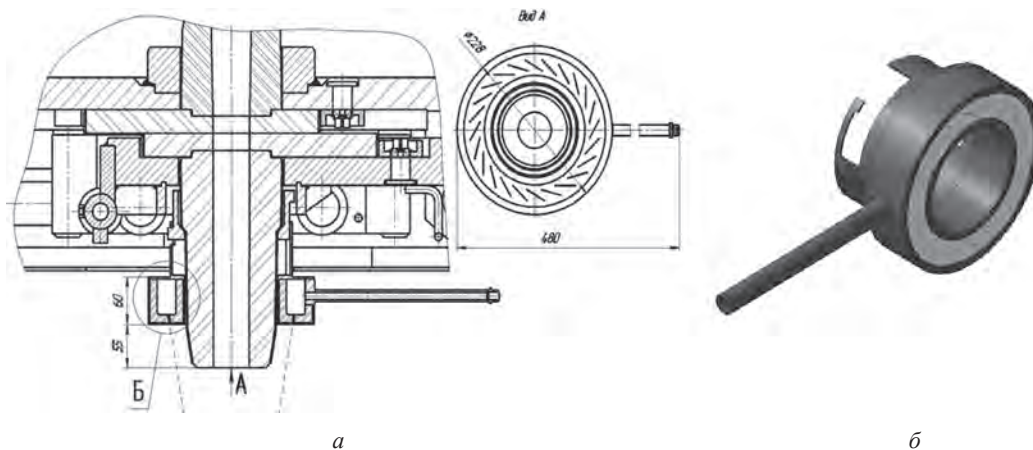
Устройство газодинамической защиты металла от вторичного окисления: *a* – схема установки устройства на шиберном затворе; *б* – модель устройства
